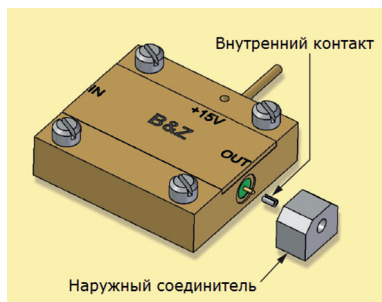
Внутренний контакт (interconnect) и наружный соединитель (outer conductor) корпуса Ultra Package
